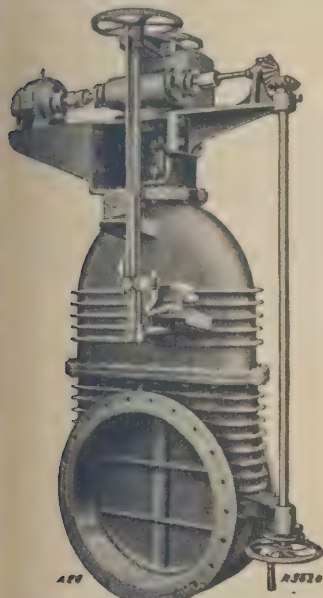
Druckschieber, 900 mm l. W. in einem Schleusenpumpenwerk.
